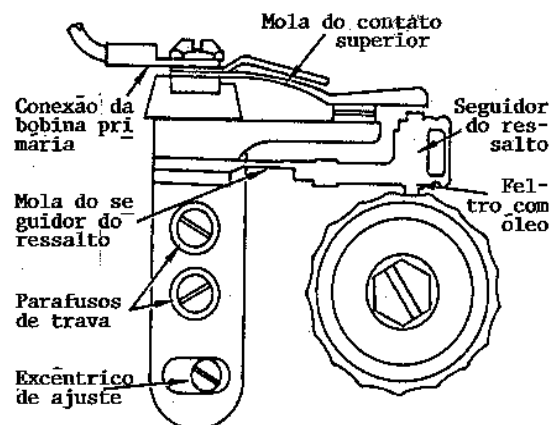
Platinado do tipo desarticulado e ressalto.
